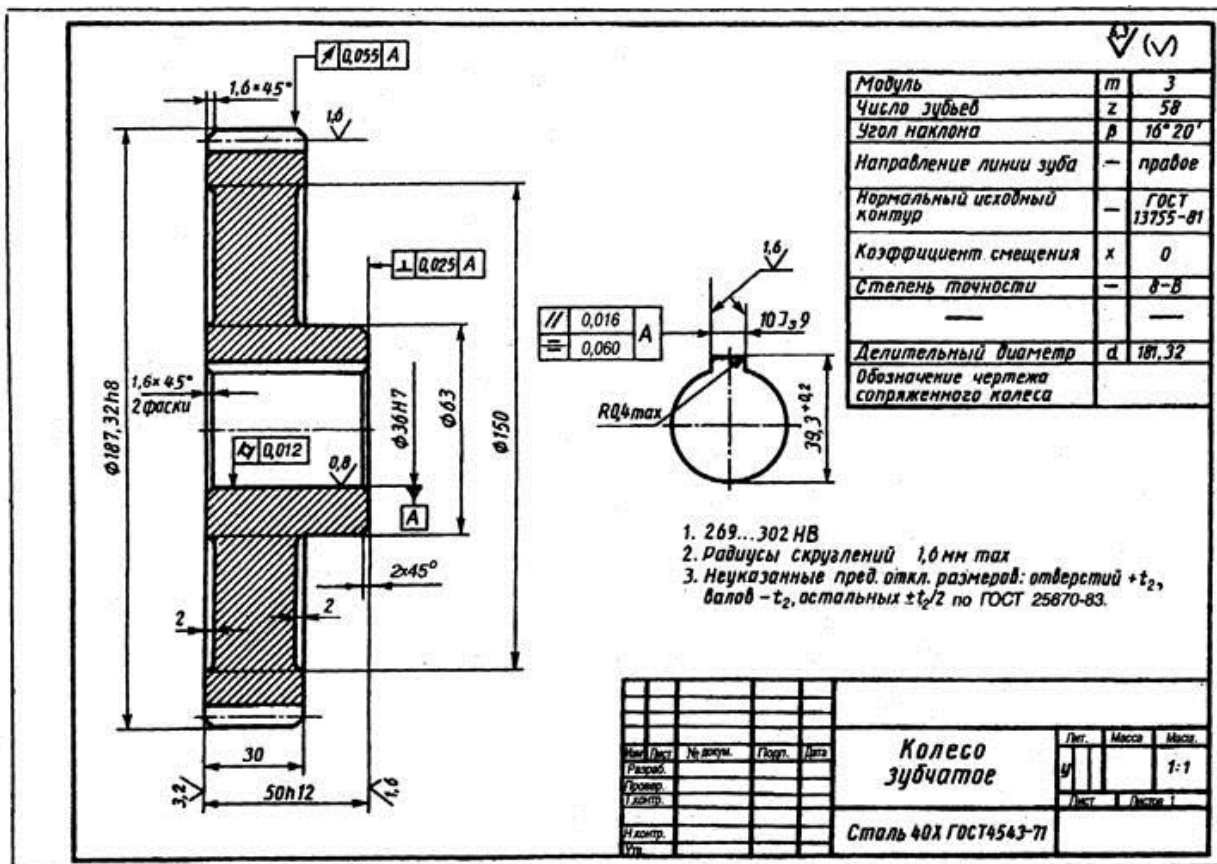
Чертёж цилиндрического зубчатого колеса редуктора
